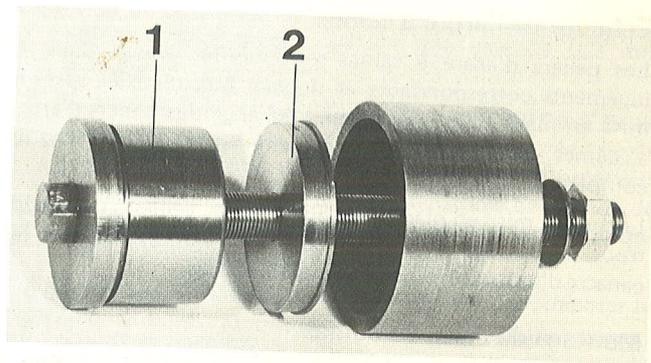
Outil 884489 pour démontage et montage des paliers de vilebrequin.
